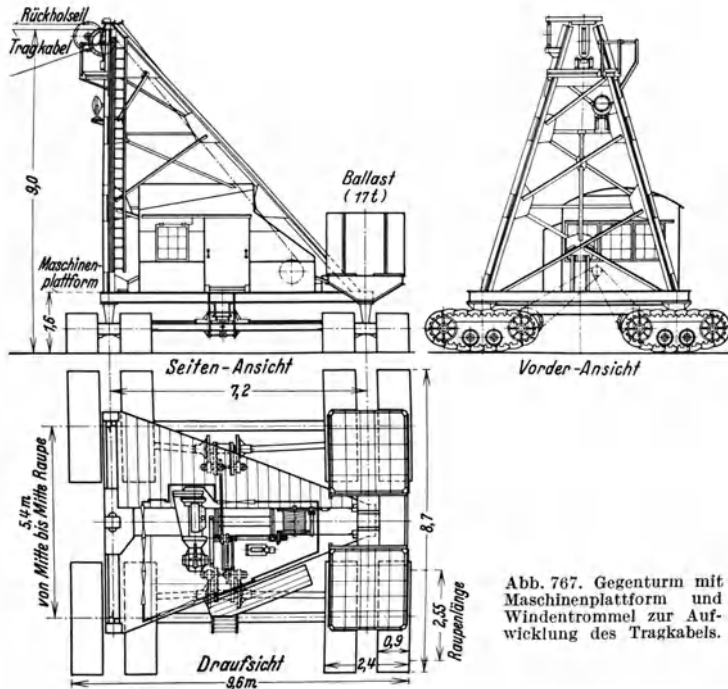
Gegenturm mit Maschinenplattform und Windentrommel zur Aufwicklung des Tragkabels.
